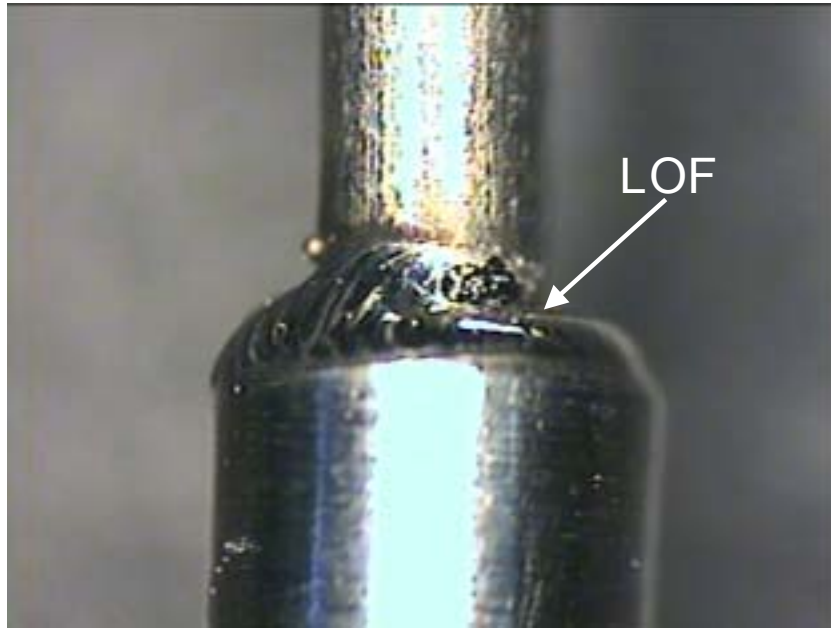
Seal tube 원주부분의 용입부족 현상 (×20)
